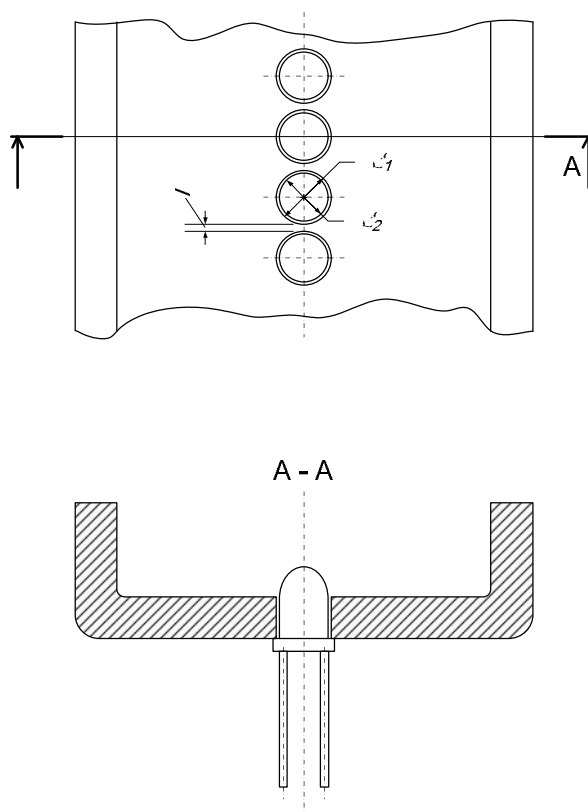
Элемент конструкции дуги для крепления фотоприёмников
